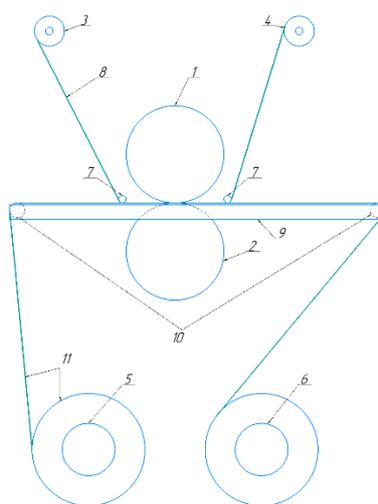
Кинематическая схема станка для тиснения: 1 — тиснильный вал; 2 — опорный вал; 3 — устройство подачи фольги; 4 — устройство смотки фольги; 5 — устройство подачи материала; 6 — устройство смотки материала; 7 — валик преднатяжитель; 8 — фольга; 9 — стол; 10 — гравитационные конвейерные ролики; 11 — материал
